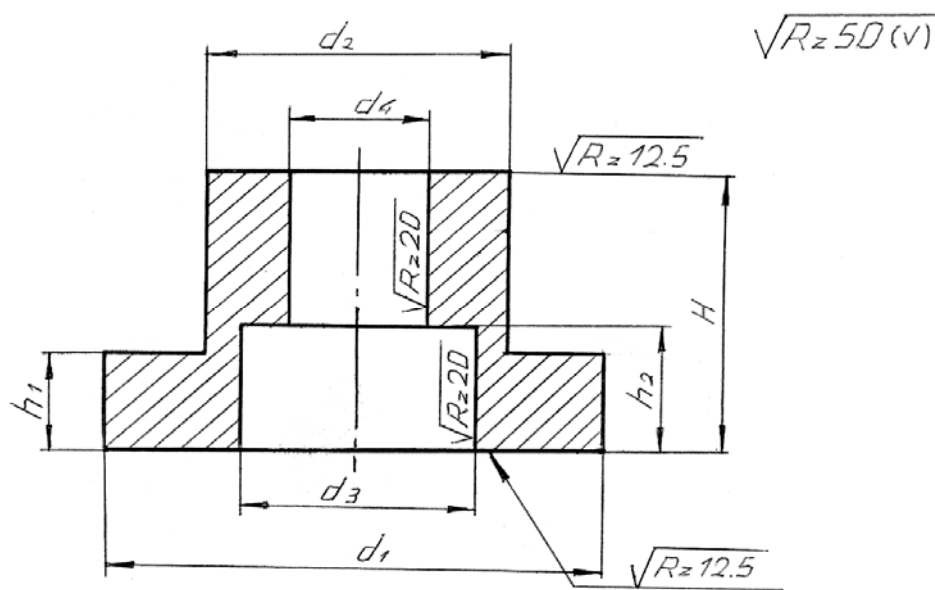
Чертёж детали: материал- сталь 45л;
